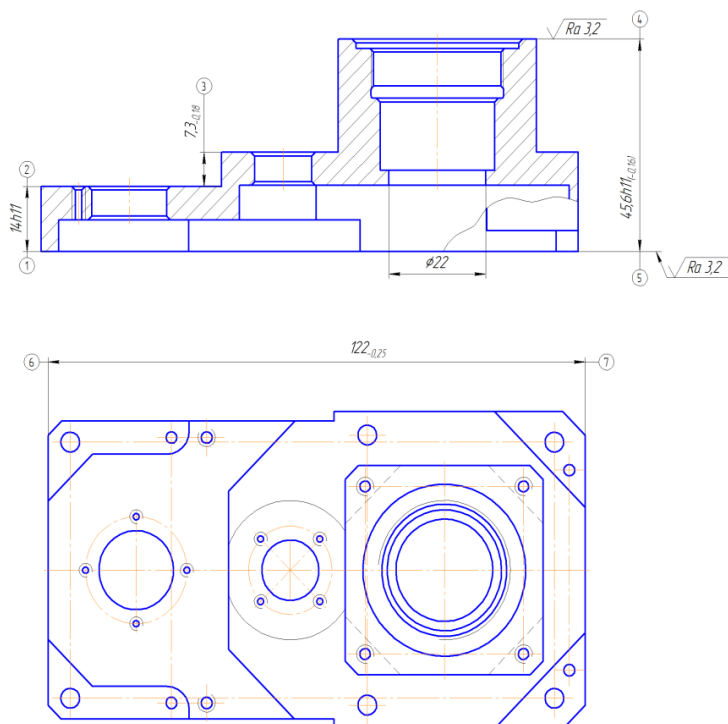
Эскиз детали «Крышка редуктора» с припусками.
